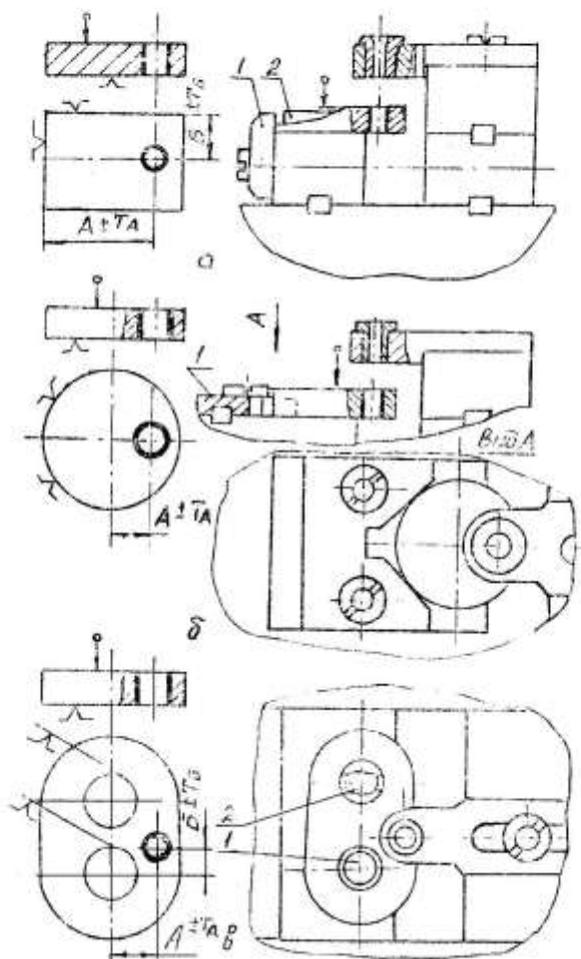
Операционный эскиз заготовки и схемы УСП для ее обработки
